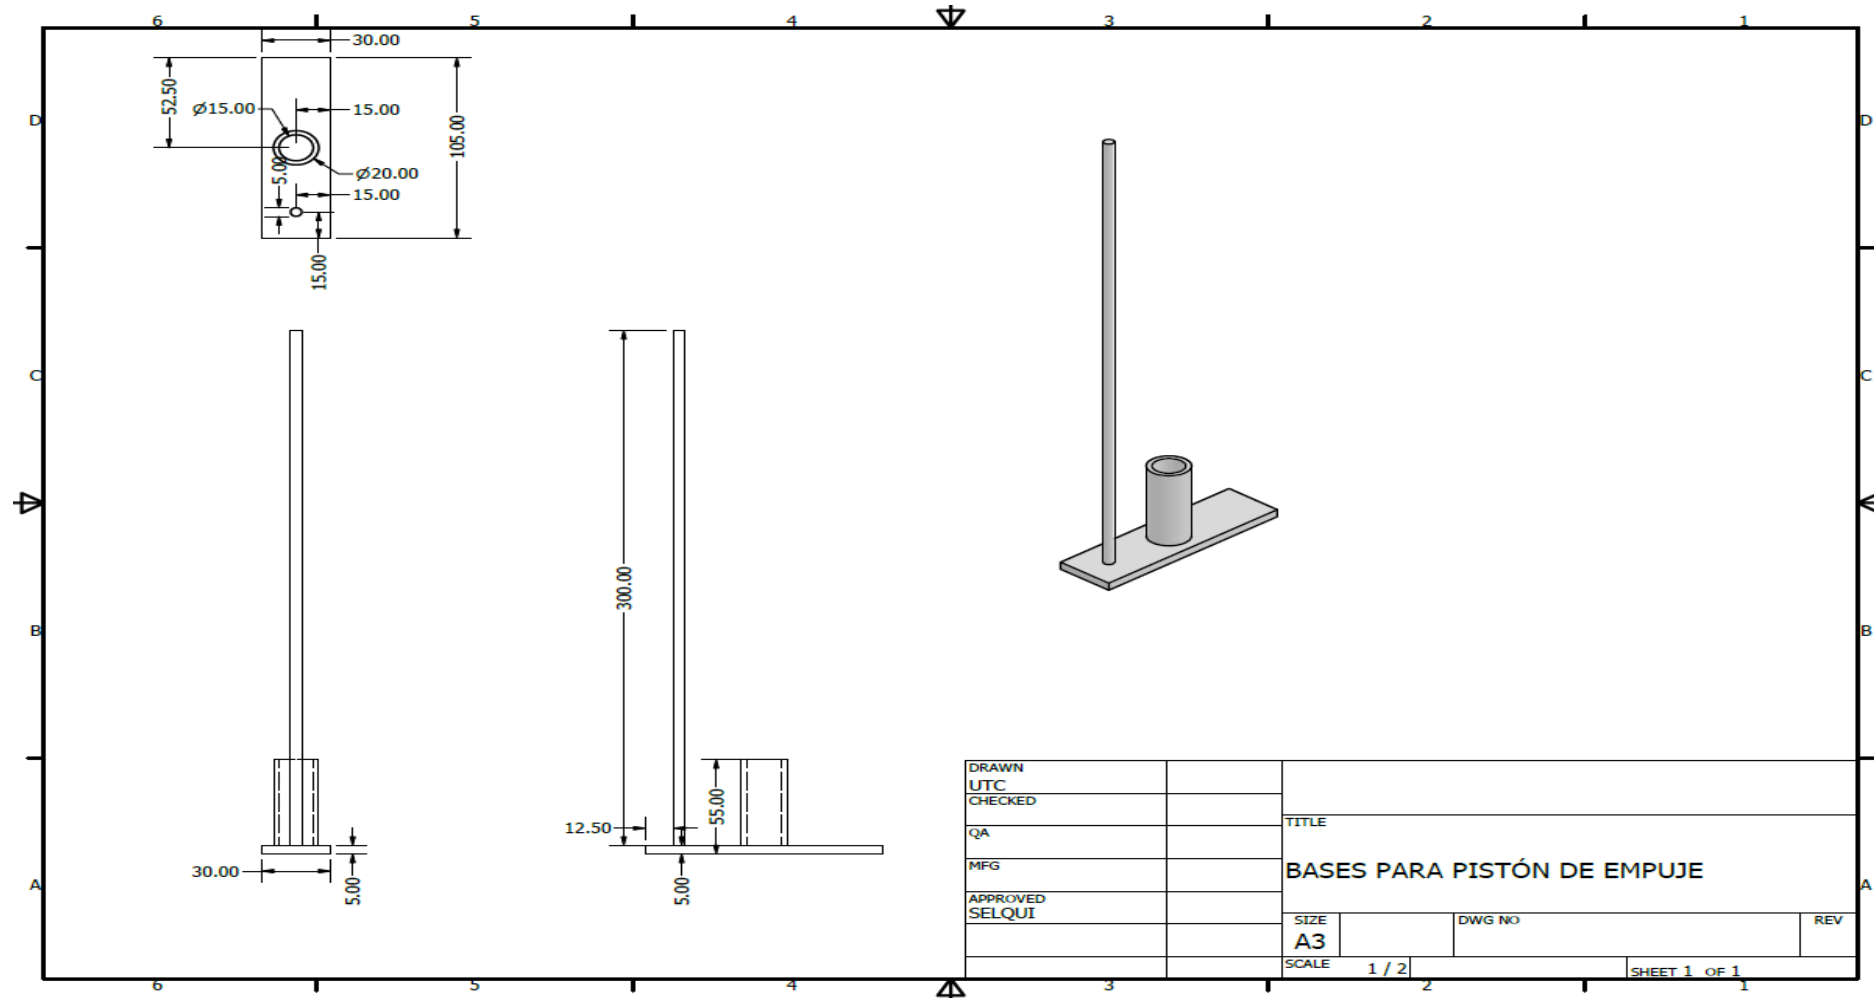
Plano de acoplamiento para el cilindro de empuje
